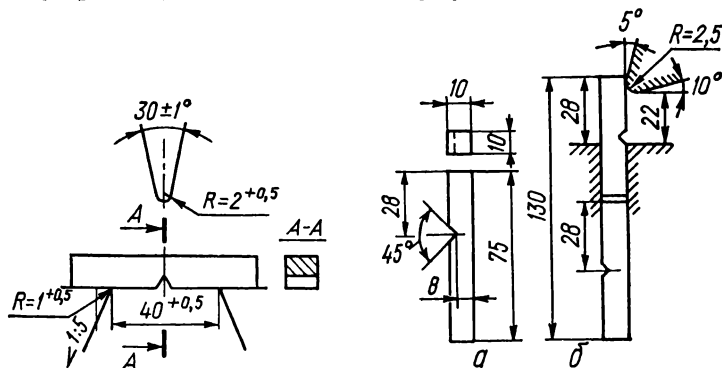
Размеры и форма стандартного ударного образца, опор и ножа маятника. Для образцов типа 20  $L = 100^{+0.5}$ .
